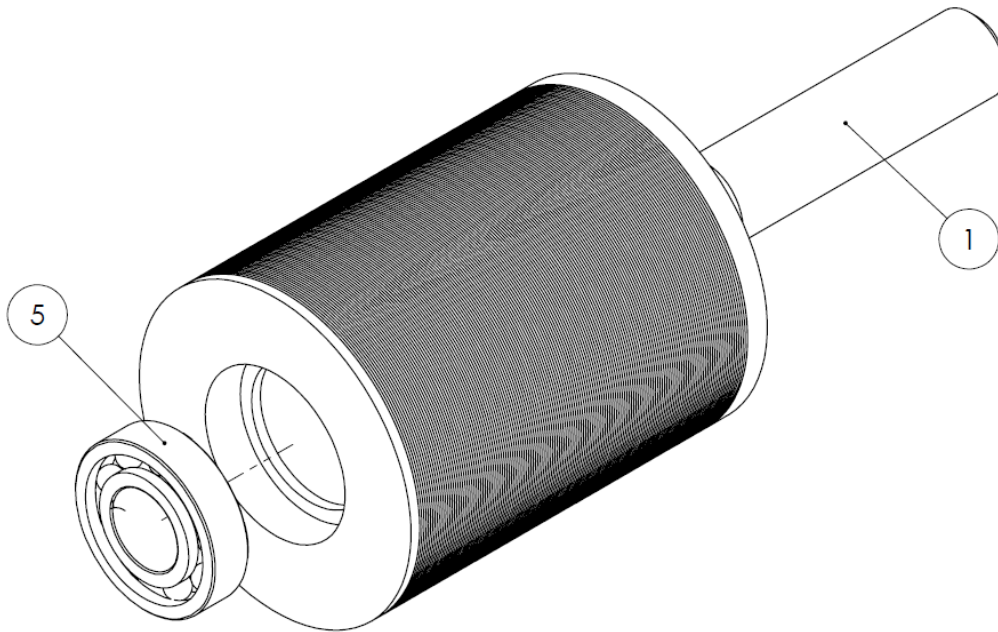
Montage du roulement à billes du rotor haute vitesse
